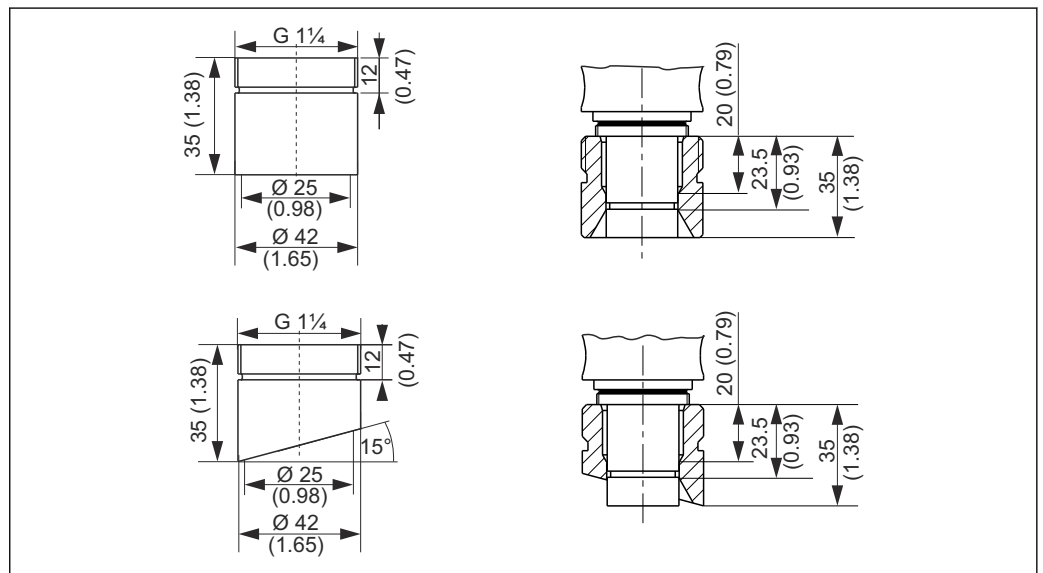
Casquillo de soldadura (boquilla de seguridad), dimensiones en mm (in)
